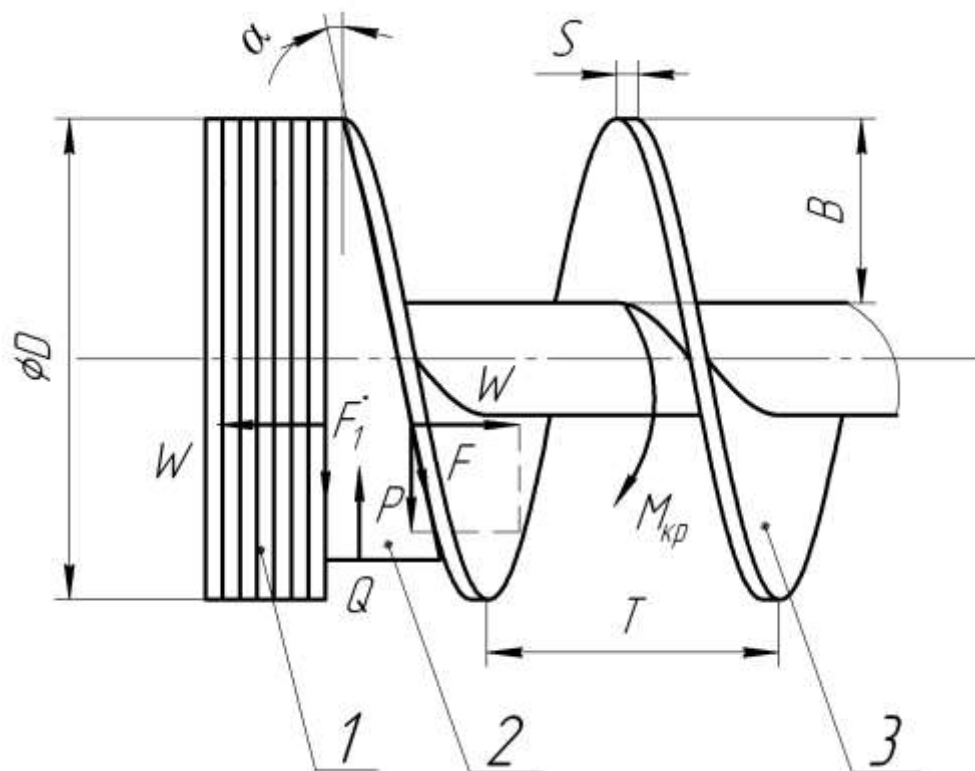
Розрахункова схема пристосування для калібрування витка гвинтової заготовки на крок: 1 – щільно навіта заготовка, 2 – клин; 3 – калібровані витки гвинтової заготовки
